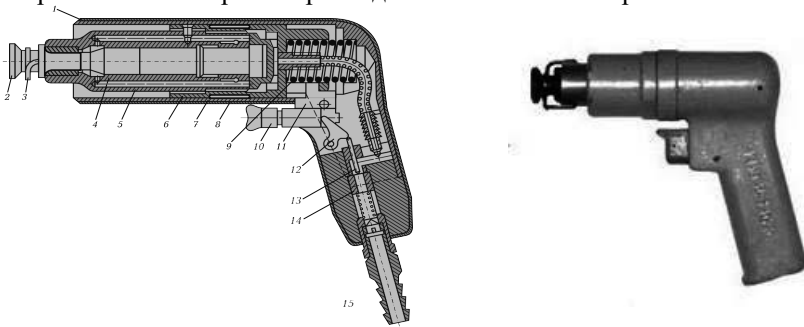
Пневматичний клепальний молоток: 1 – корпус; 2 – ударник; 3,9 – пружини; 4 – молоток; 5 – циліндр; 6 – стакан; 7 – золотник; 8 – кришка; 10 – курок; 11 – рукоятка; 12 – важіль; 13 – штовхач; 14 – пусковий клапан
